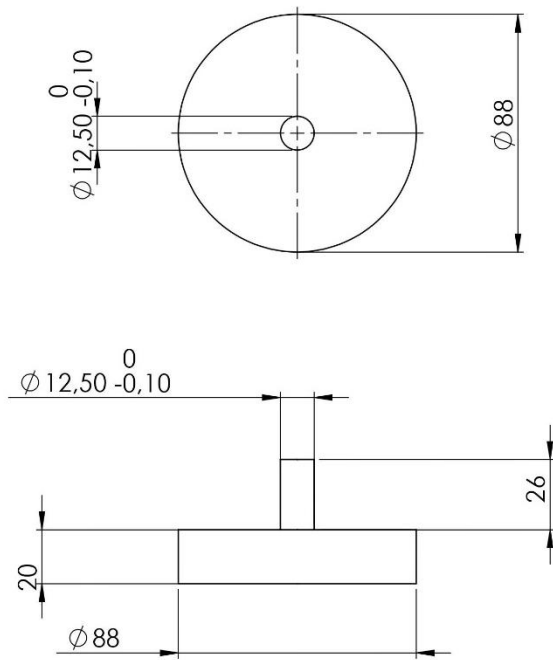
Desenho técnico da peça punção do conjunto de prensagem.
